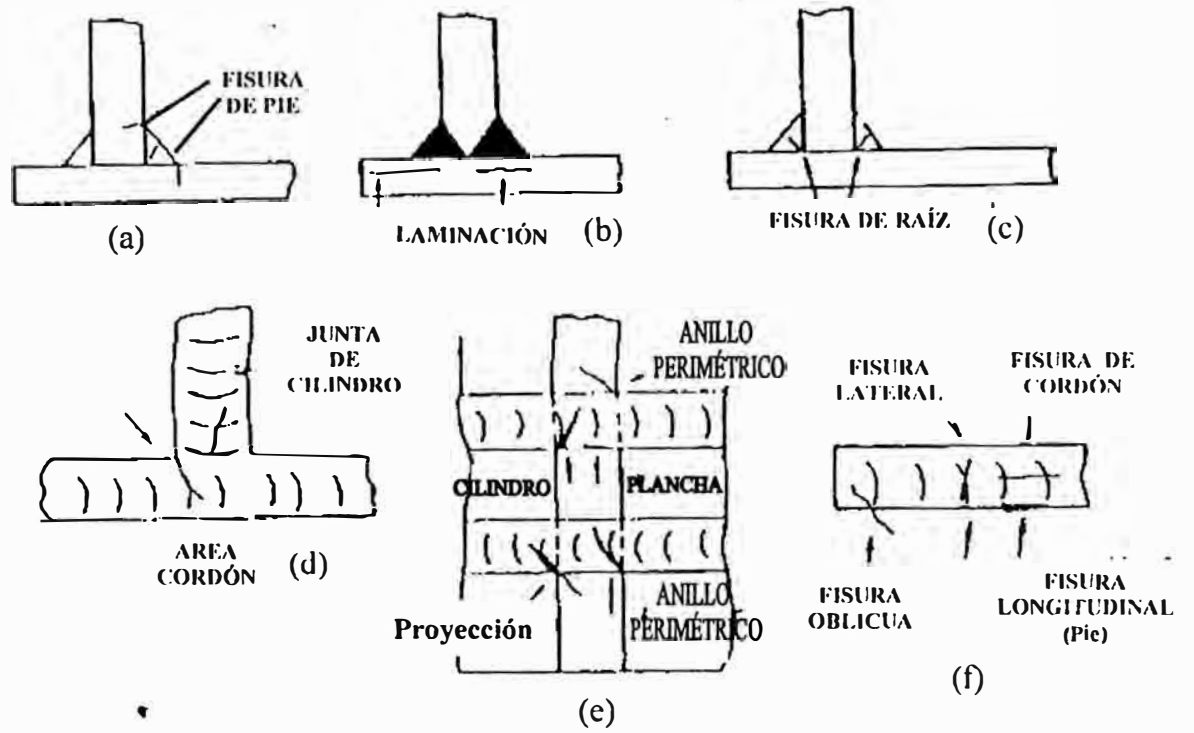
Fisuras en junta de cilindro y anillo perimétrico del fondo.
